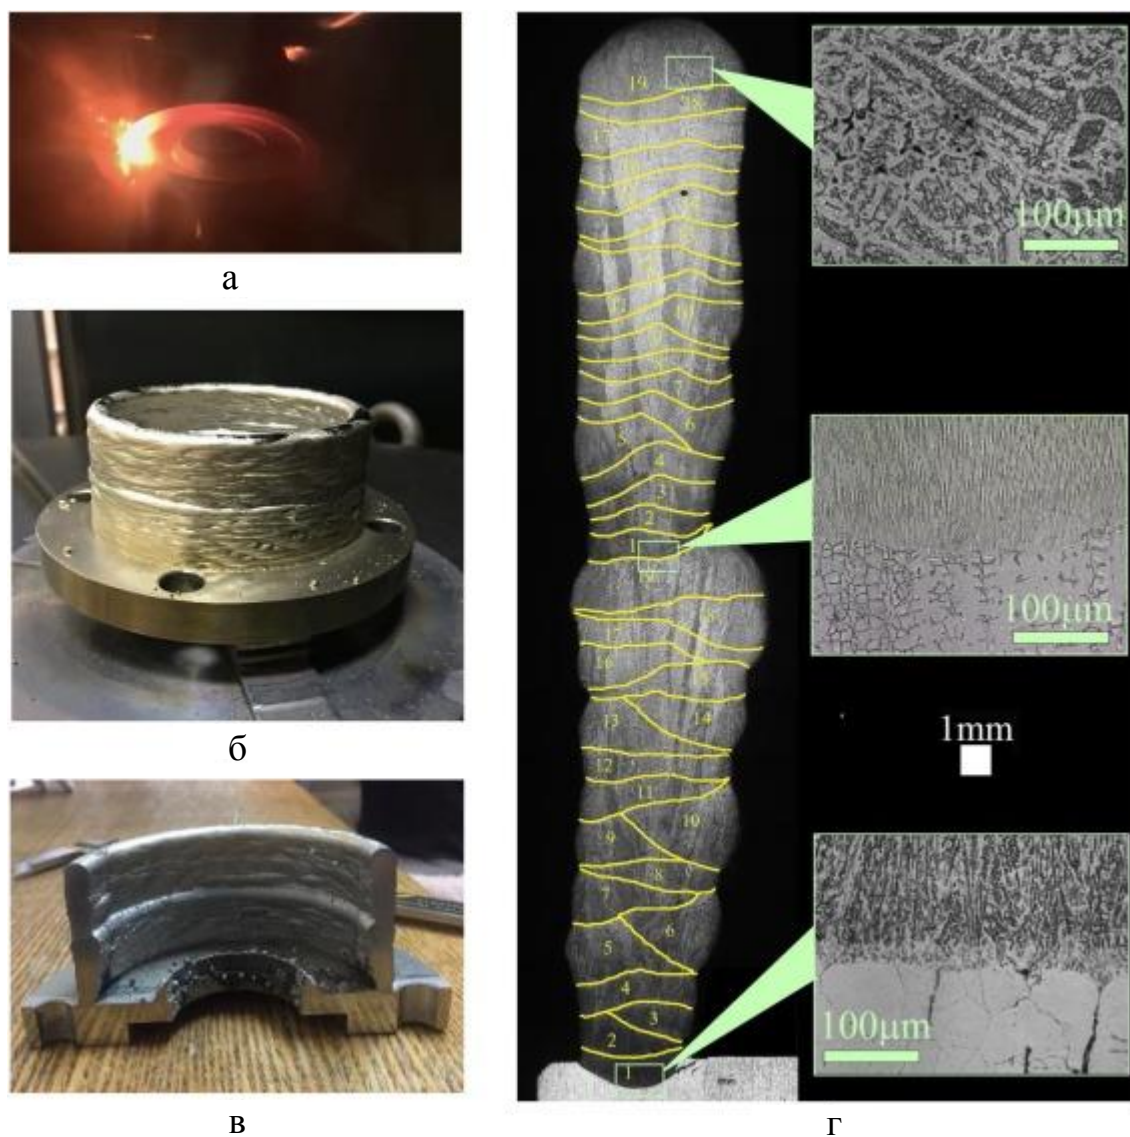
Процесс изготовления цилиндрической конструкции (а), полученное изделие (б, в) и его макросечение (г)
